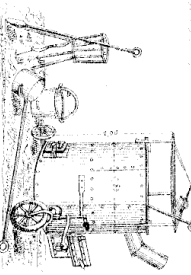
Machine à vapeur par M. Henry Teley et Co.
